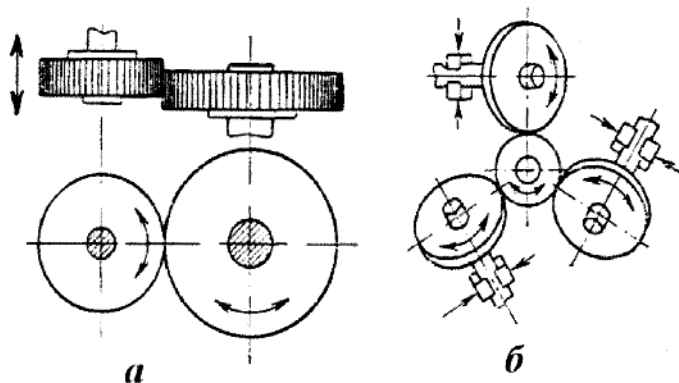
Схемы притирки зубьев цилиндрических зубчатых колес: а - с параллельными осями притиров; б - со скрещивающимися осями притиров.
